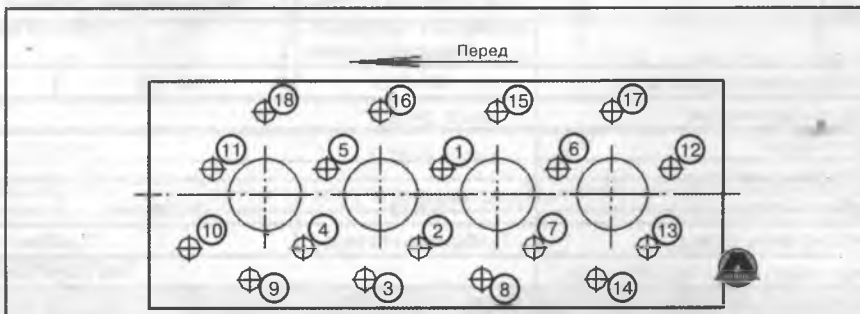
Порядок подтяжки гаек головки блока цилиндров
